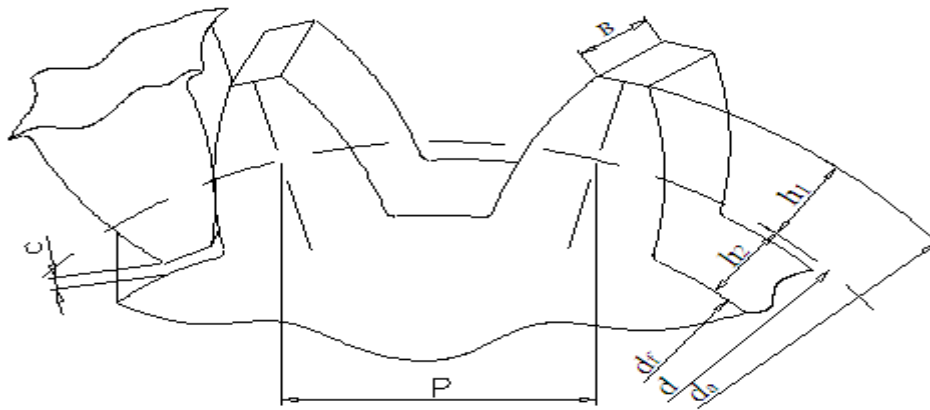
Схема евольвентного зубчастого зачеплення циліндричної прямозубої передачі
